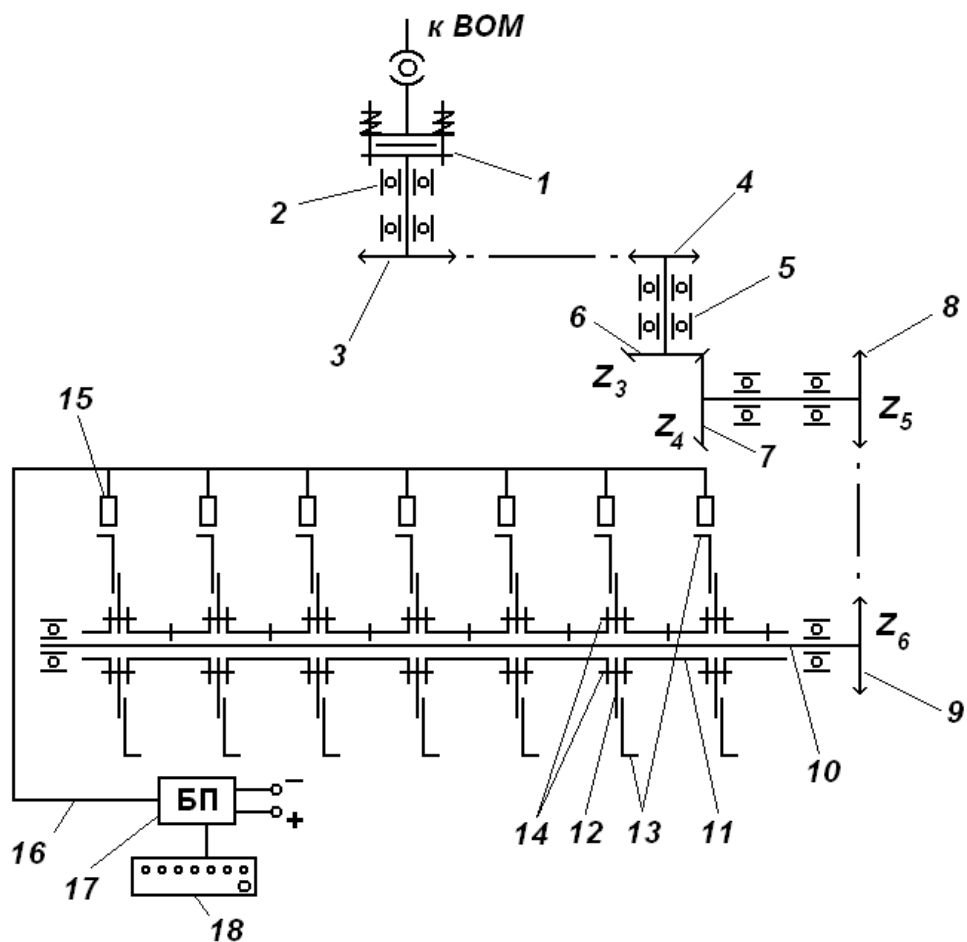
Кинематическая схема фрезы со срезными болтами секций: 1-фрикционная муфта; 2- подшипниковый узел; 3- звездочка подшипникового узла; 4- звездочка входного вала конического редуктора; 5 – подшипниковый узел редуктора; 6,7 – конические шестерни редуктора; 8- звездочка выходного вала редуктора; 9- звездочка фрезерного барабана; 10- вал барабана фрезы; 11- распорная втулка; 12 – диск секции; 13 – ножи; 14- срезные болты; 15 – датчик Холла; 16 – шина; 17 – блок программирования; 18 – индикатор срабатывания секций.
